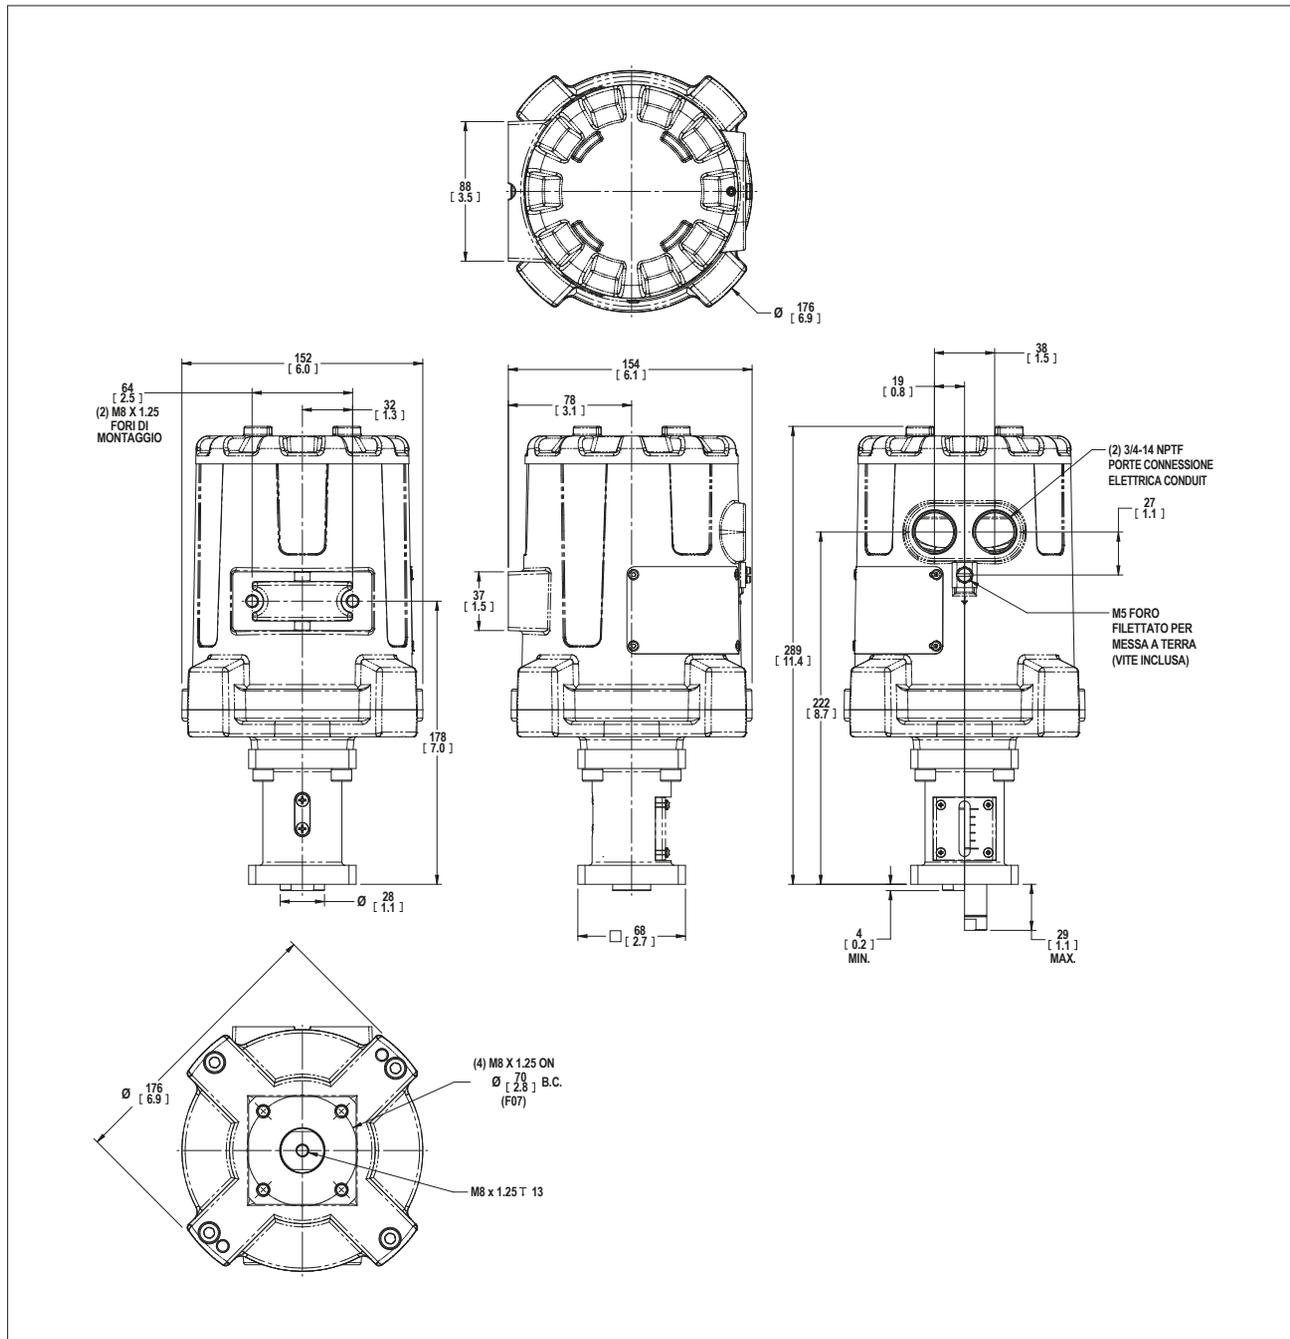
Dimensioni di installazione dell'attuatore PAXL
